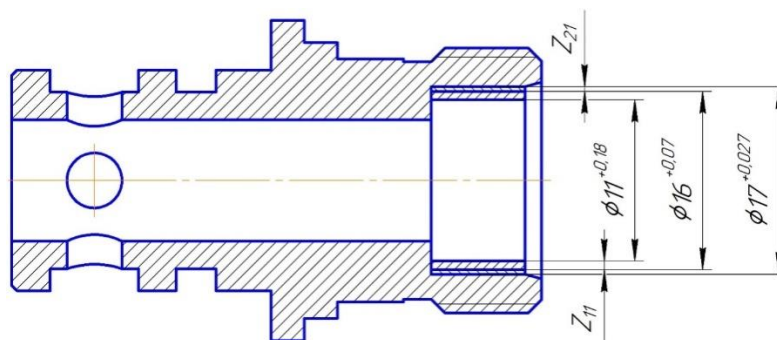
Эскиз диаметрального припуска для размера 17H8
